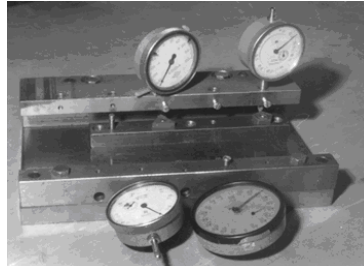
Приспособление для измерения высоты h в вершинах пластин
